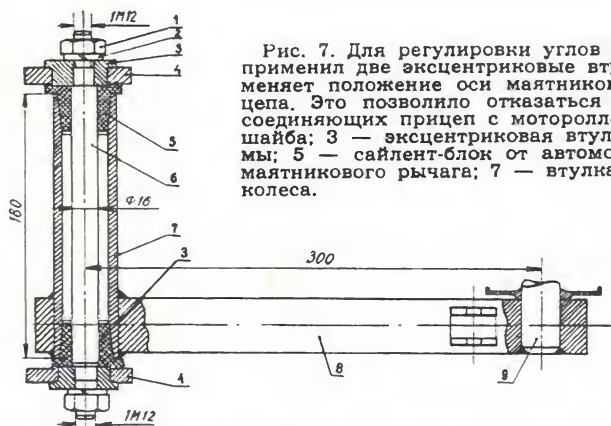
Для регулировки углов установки колес автор применил две эксцентриковые втулки, поворот которых меняет положение оси маятниковой вилки колеса прицепа. Это позволило отказаться от регулируемых тяг, соединяющих прицеп с мотороллером: 1 — гайка; 2 — шайба; 3 — эксцентриковая втулка; 4 — проушина рамы; 5 — сайлент-блок от автомобиля ГАЗ-21; 6 — ось маятникового рычага; 7 — втулка; 8 — рычаг; 9 — ось колеса.
